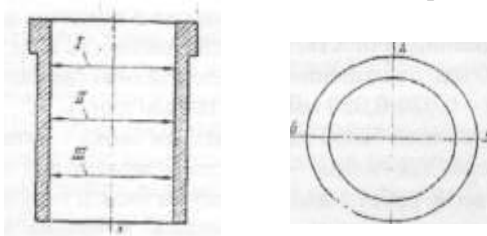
Схема обмера отверстия под поршень в гильзе цилиндра
